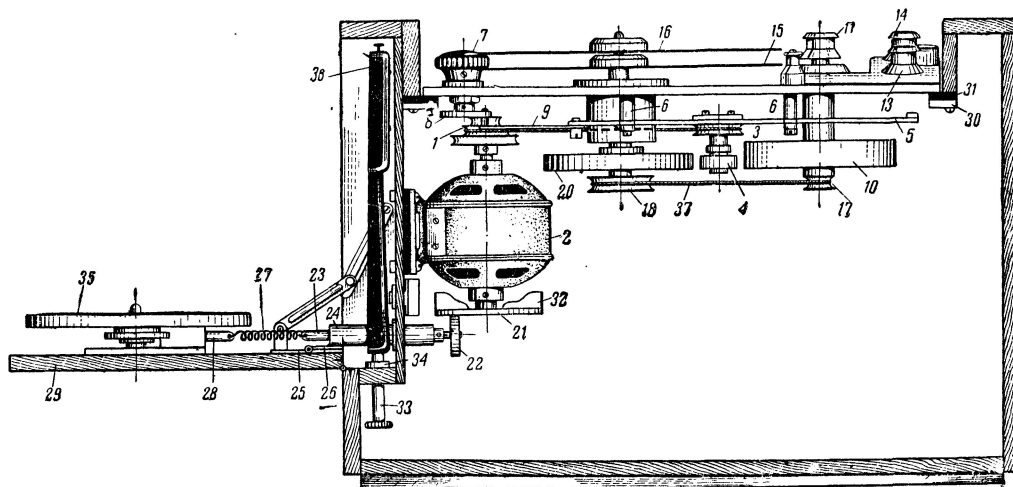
Расположение деталей лентопротяжного механизма и проигрывателя граммофонных пластинок (вид в разрезе со стороны передней панели)
